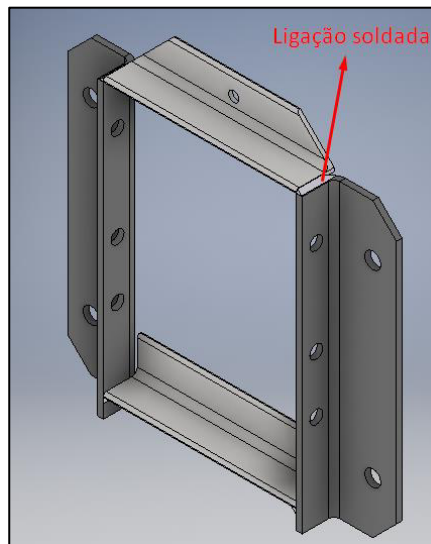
Estrutura de ligação à torre – carrinho.
